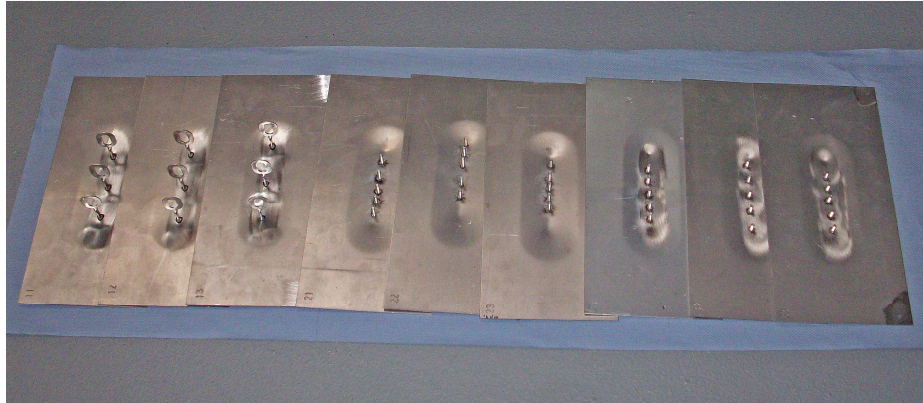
Probebleche mit aufgeschweißten Bits/Bolzen
